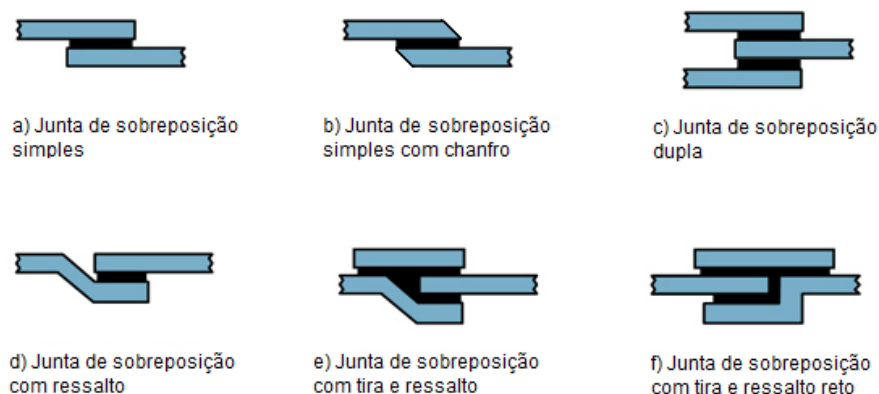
Diferentes configurações de juntas de sobreposição. Adaptado de: *Mapeng – Assembly considerations, Joint Design* [19].
